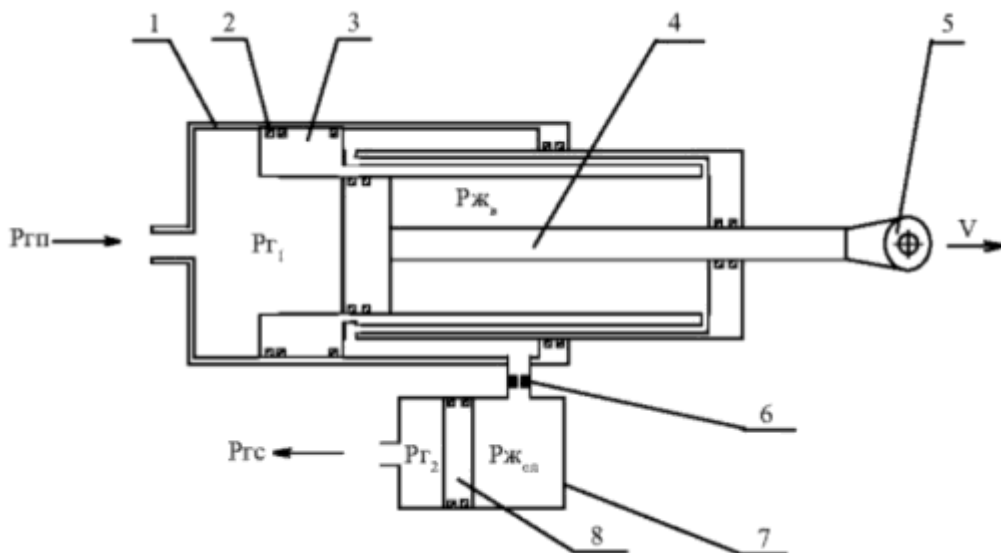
Конструктивная схема привода газогидравлического [6]: 1 – цилиндрический корпус ПГГ; 2 – уплотнения подвижных элементов; 3 – промежуточный поршень; 4 – шток; 5 – серьга крепления штока ПГГ на выдвигном насадке сопла; 6 – дроссель слива жидкости; 7 – бачок слива гидравлической жидкости; 8 – плавающий поршень бачка слива. Обозначения для выдвигания штока: $P_{гп}$ – газовое давление питания; $P_{г1}$ – давление в рабочей газовой полости; $P_{жв}$ – давление в подпоршневой жидкостной полости; $P_{жсл}$ – давление в жидкостной полости слива; $P_{г2}$ – давление в газовой полости блока слива; $P_{гс}$ – давление в среде сброса давления из газовой полости блока слива.
